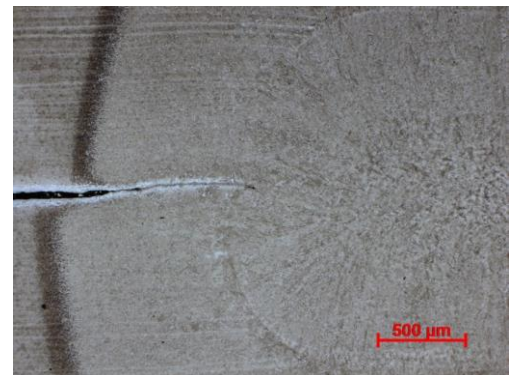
Abb. III: Gefügebewertung einer Punktschweißnaht
